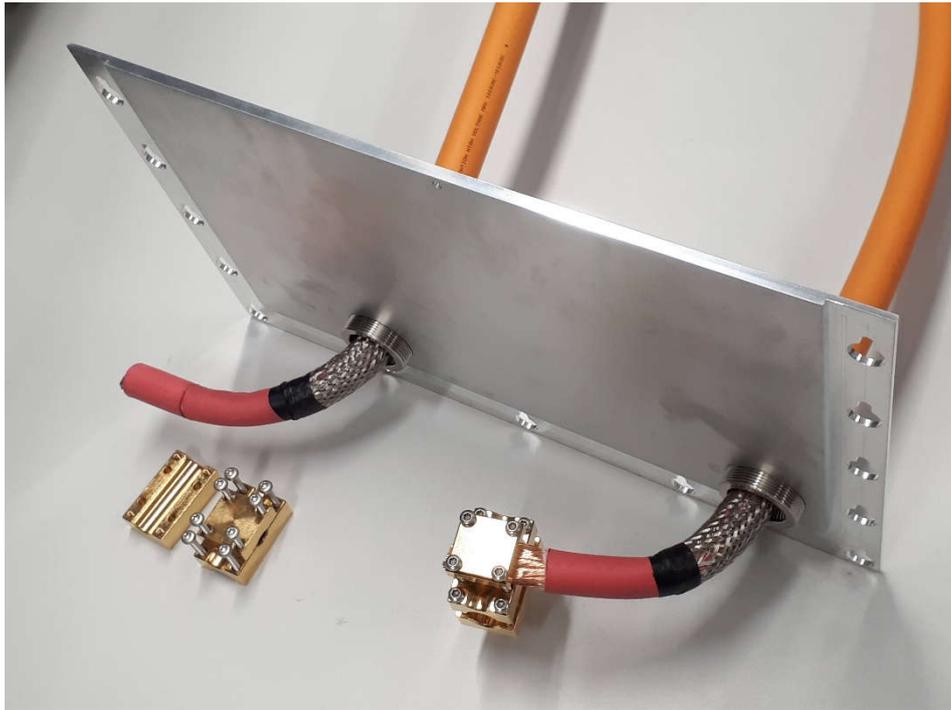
Flanschplatte mit HV-Kabeln, eine Klemme bereits montiert
